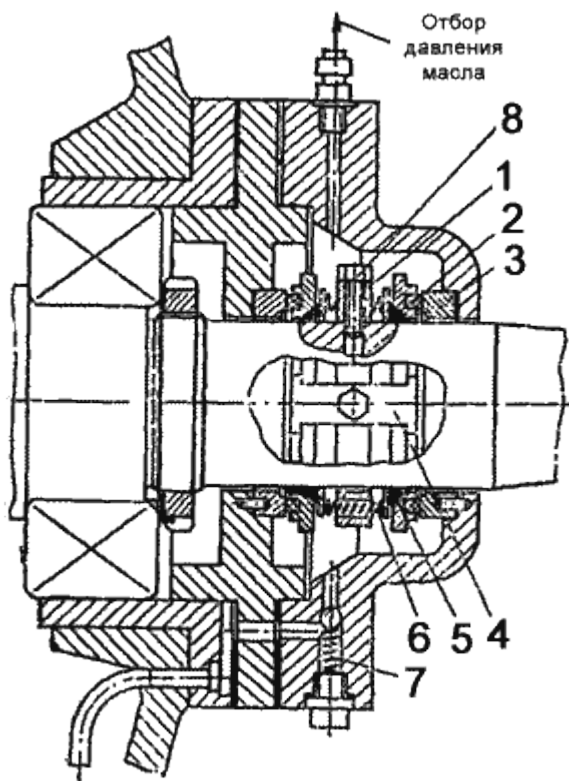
Сальник компресора: 1 - обойма; 2 - кільце графітове; 3 - кільце сталеве; 4 – планка; 5 - фторопластовий манжет; 6 – пружина; 7 - перепускний регулюючий клапан; 8 – гвинт стопорний
